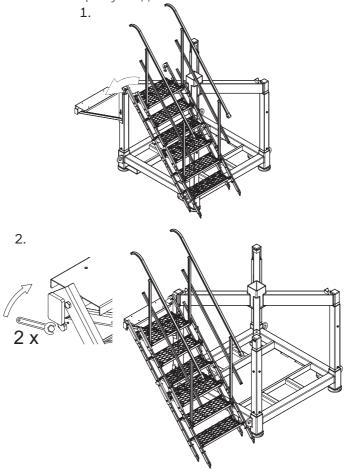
Установите боковую лестницу на кронштейн лестницы 8890. Проверьте лестницу на площадке UI перед установкой
